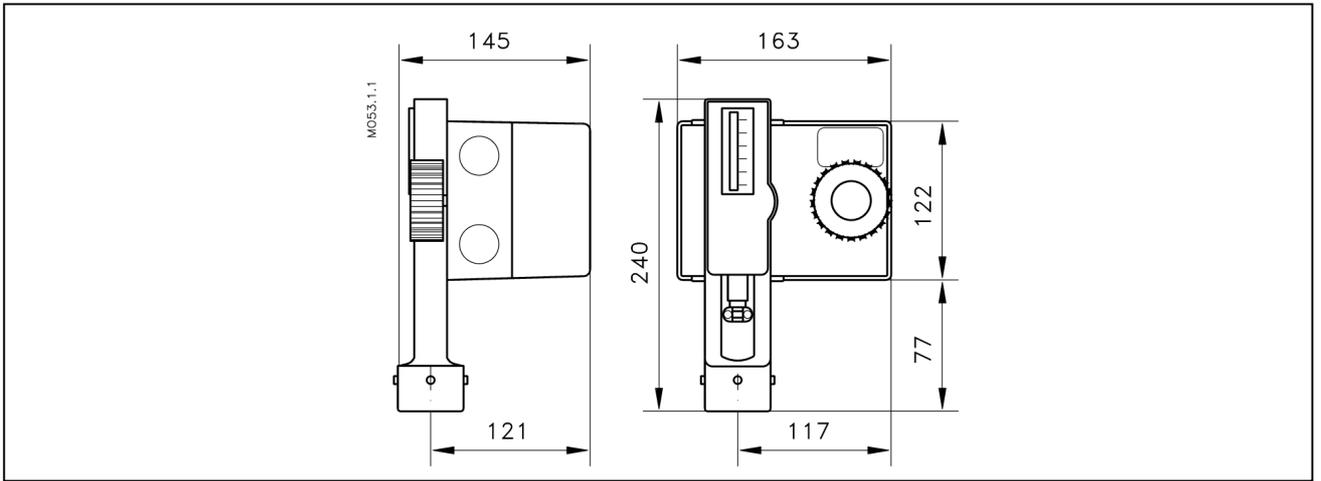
Габаритные и присоединительные размеры AMV 323, 423, 523.
